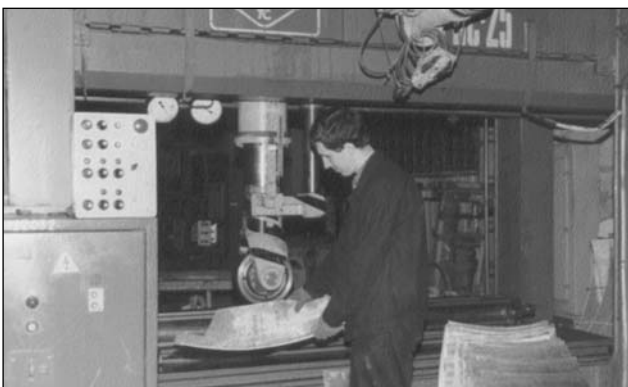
Гибка листовых деталей обшивки диффузора на станке МГПС-25
